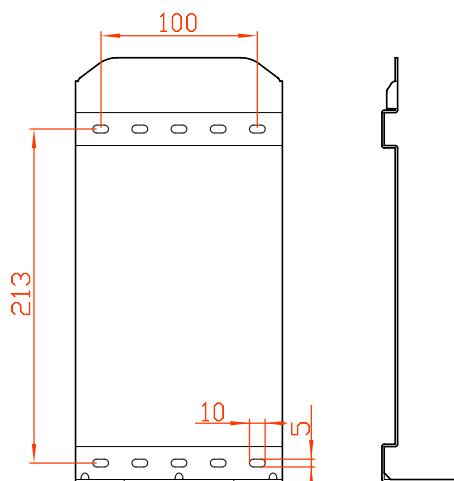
Dimensões da instalação otimizada (unidade: mm)
